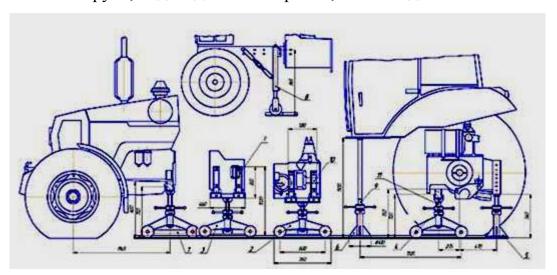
Схема стенда стенд ОР-Ш46-ГОСНИШ.
